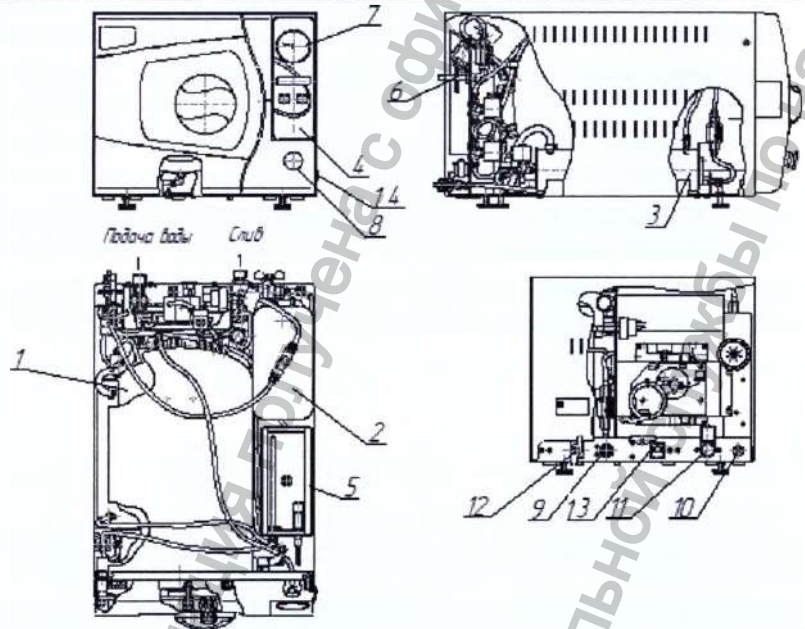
Внешний вид стерилизатора парового ГКа-25-ПЗ в варианте исполнения КИУС.942711.004-04.
